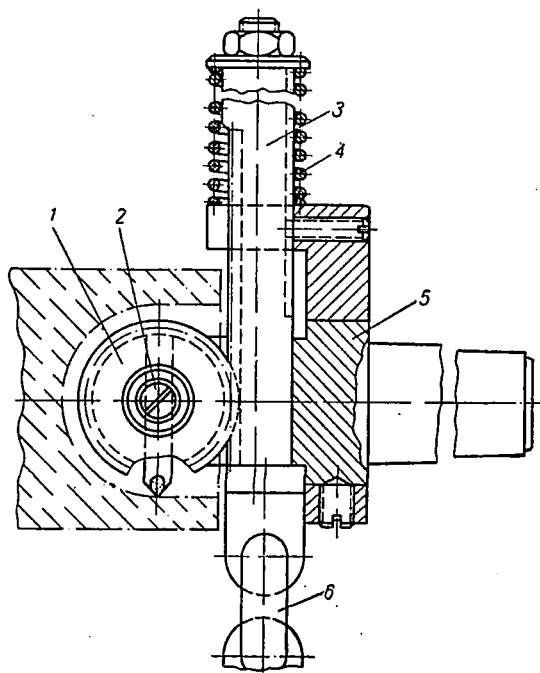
Приспособление для расточки внутренних сферических поверхностей.
